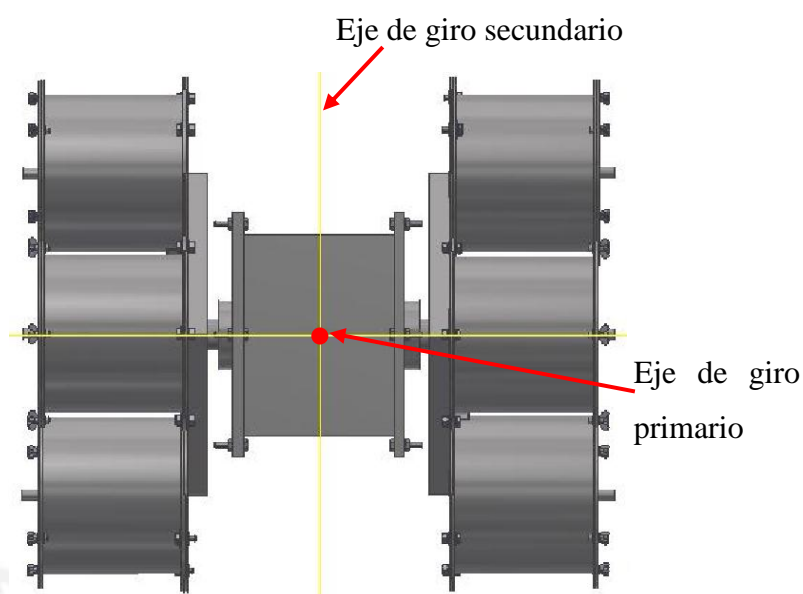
Acercamiento al conjunto de moldes en vista frontal.
